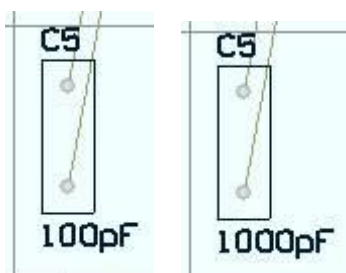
80 更新前的 PCB 图 5 — 81 更新后的 PCB
